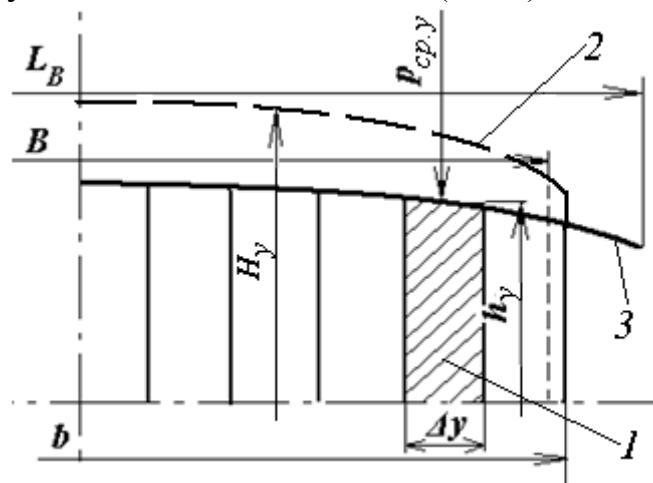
Розрахункова схема: 1 - елемент штаби; 2 – підкат; 3 - робочий профіль робочого валка
